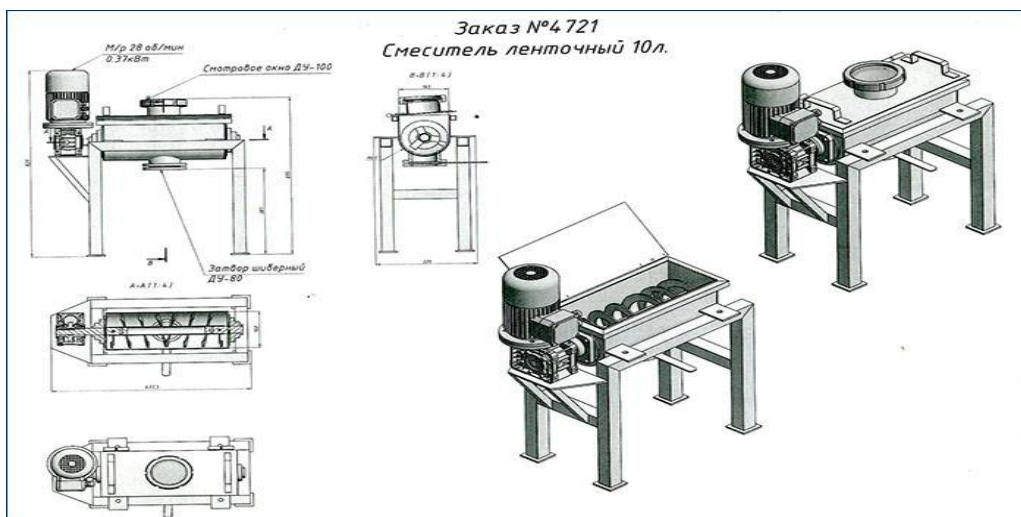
Стрічковий змішувач 10л - схема пристрою.
